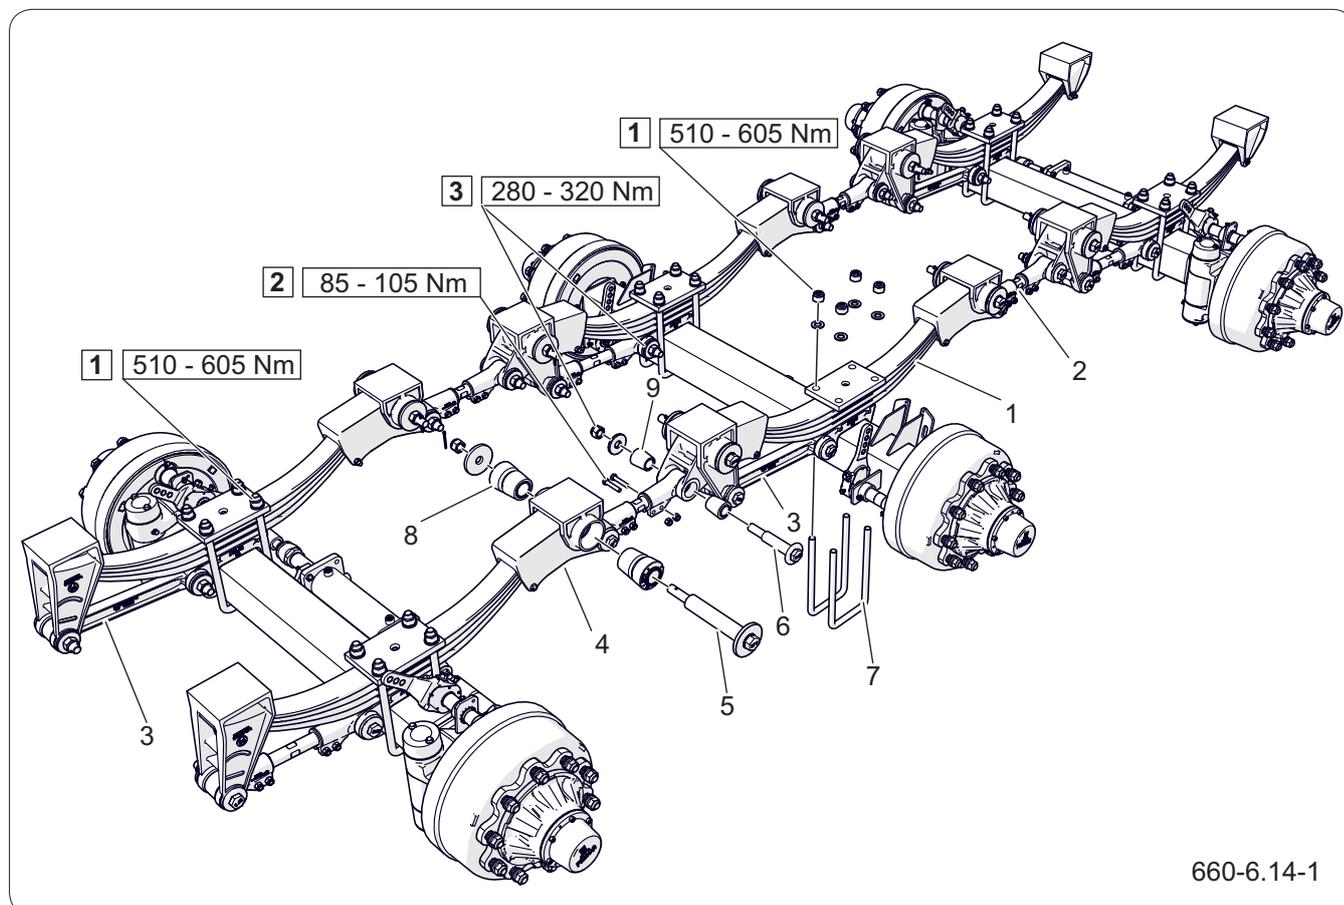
Работа механической подвески тридем, ось установлена под рессорой (1) пружина, (2) регулируемое соединение, (3) жесткое соединение, (4) рычаг, (5) «шпилька» подвески, (6) крепление рессоры, (7) винт крепления оси «U», (8) (9) металлорезиновая втулка
